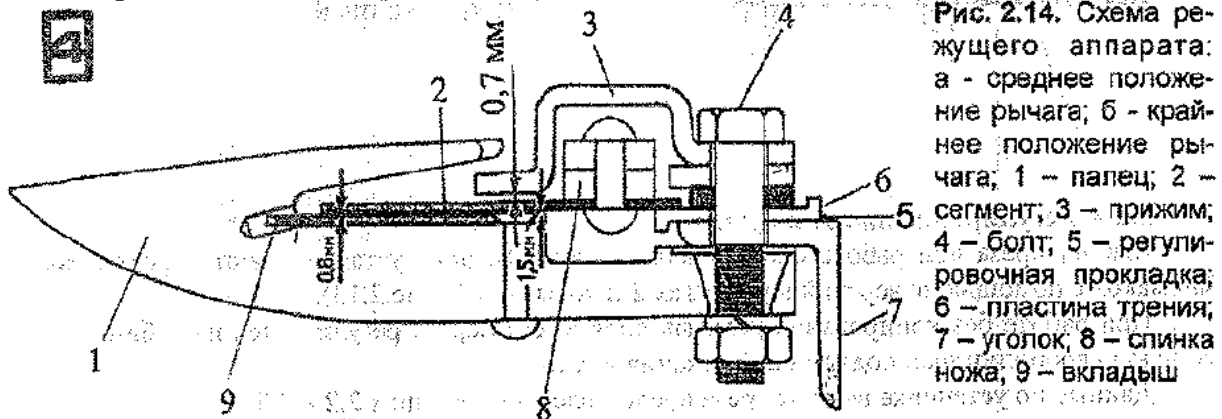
Схема режущего аппарата: а - среднее положение рычага; б - крайнее положение рычага; 1 - палец; 2 - сегмент; 3 - прижим; 4 - болт; 5 - регулировочная прокладка; 6 - пластина трения; 7 - уголок; 8 - спинка ножа; 9 - вкладыш
